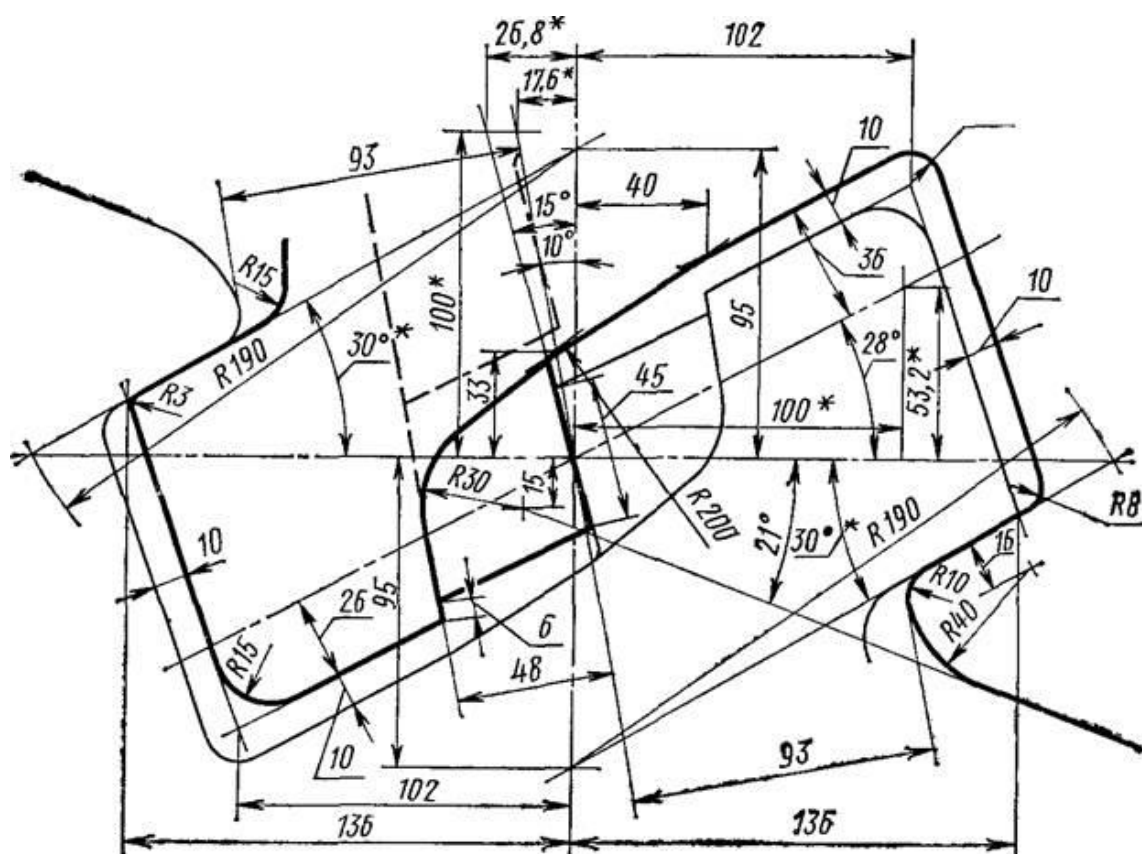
Размеры контура зацепления автосцепного устройства
